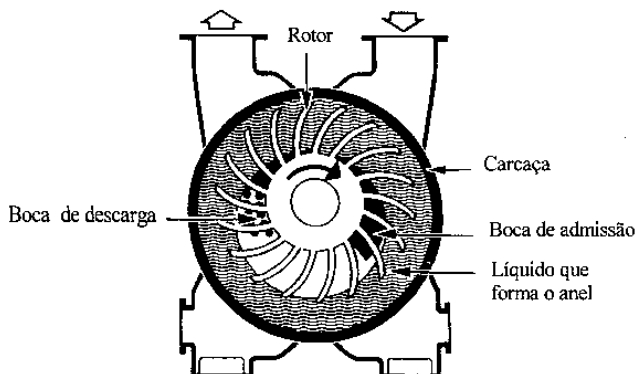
Compressor ou bomba de vácuo de anel líquido (Fonte: Atlas Copco).
